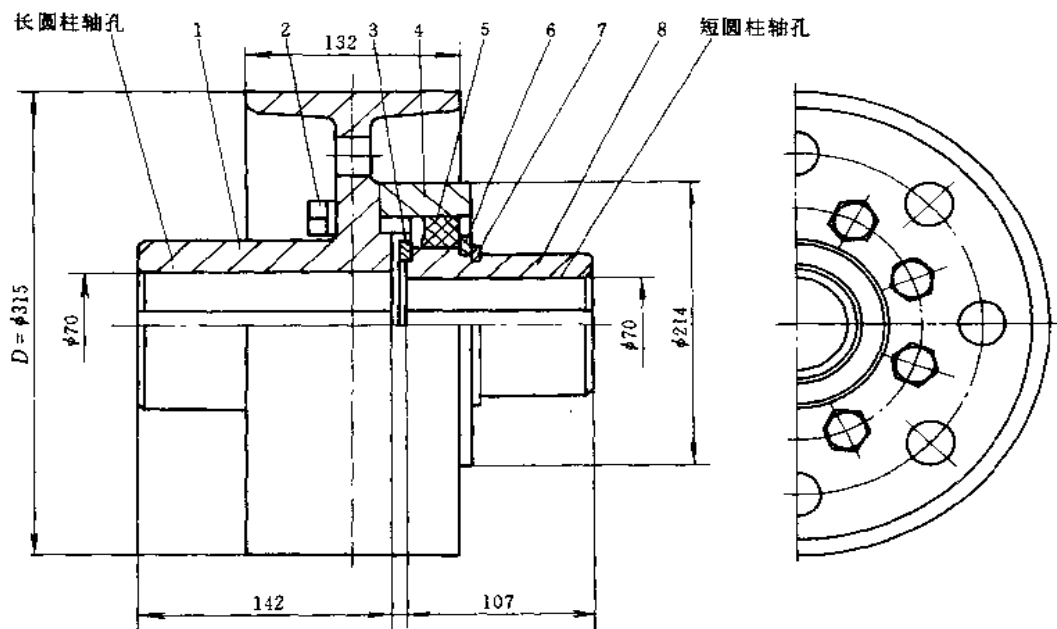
带制动轮弹性柱销齿式联轴器 (ZLL 型)
